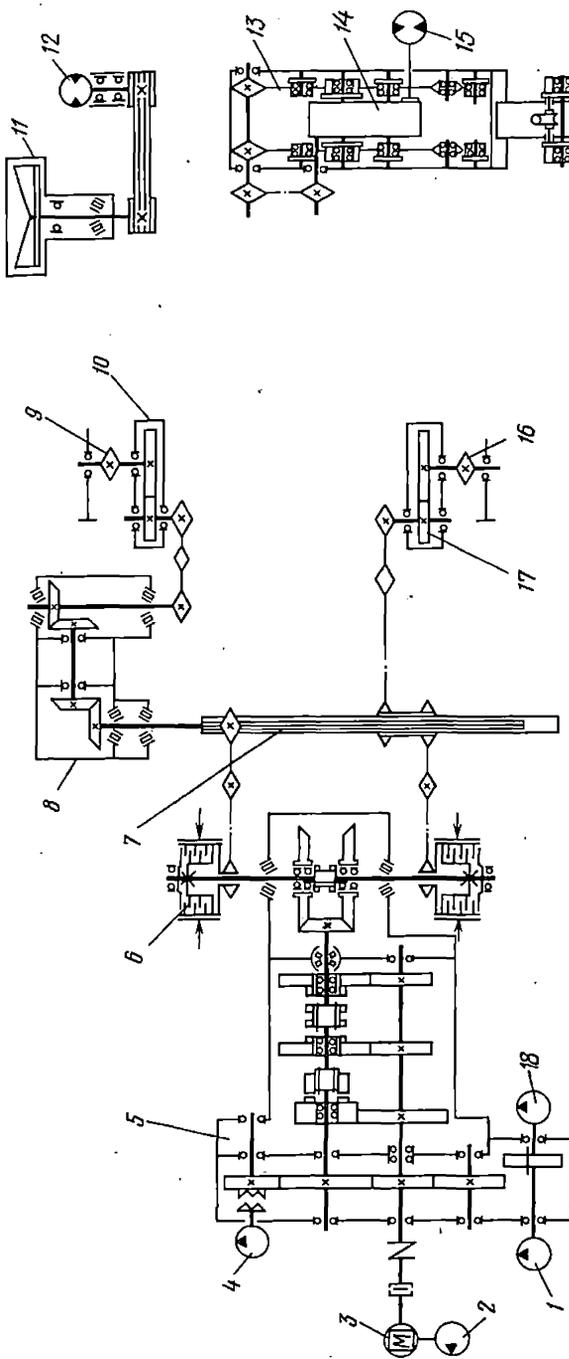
Кинематическая схема экскаватора ЭМ-152Б.
